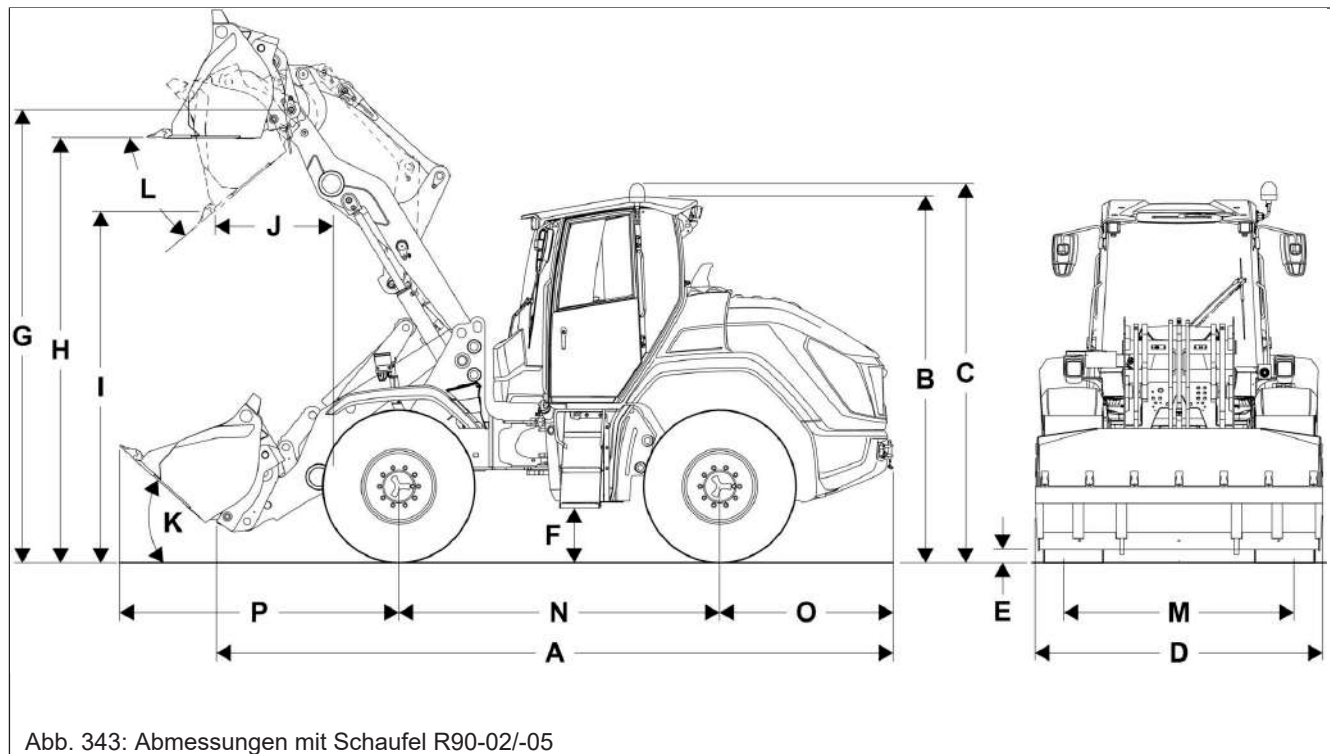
Abmessungen mit Schaufel R90-02/-05
